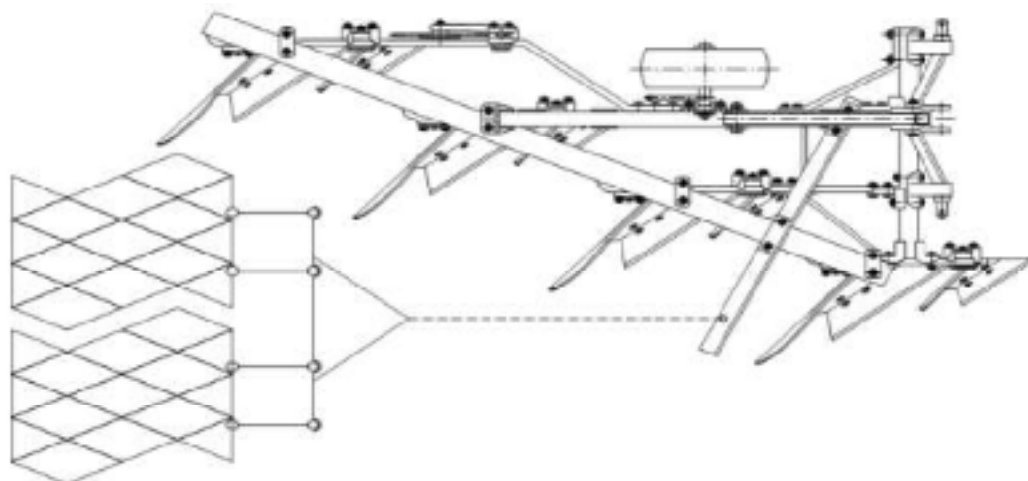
Комбинированный пахотный агрегат с зубчатыми боронами, присоединенными с помощью цепи.
